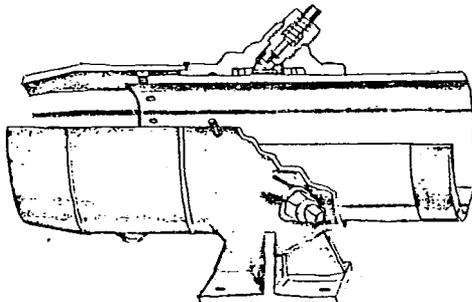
Junta de expansión de casquillo es básicamente un cilindro que se desliza sobre otro. Absorbe movimientos axiales grandes, pero nada de movimientos angulares. Deben tener empaques y estar localizados en lugares de fácil acceso.
